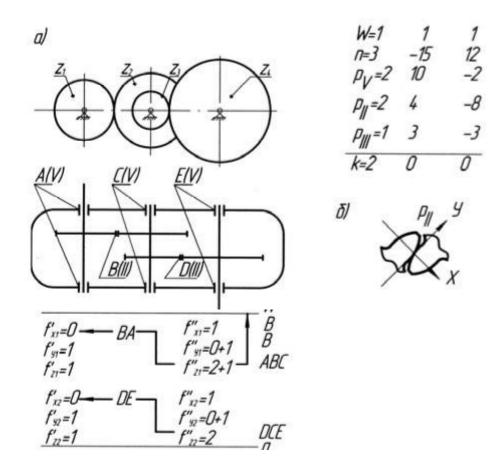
Модернизированный редуктор: а – кинематическая схема; б – контакт зубьев второй ступени редуктора; с – таблица распределения подвижностей в кинематических парах
